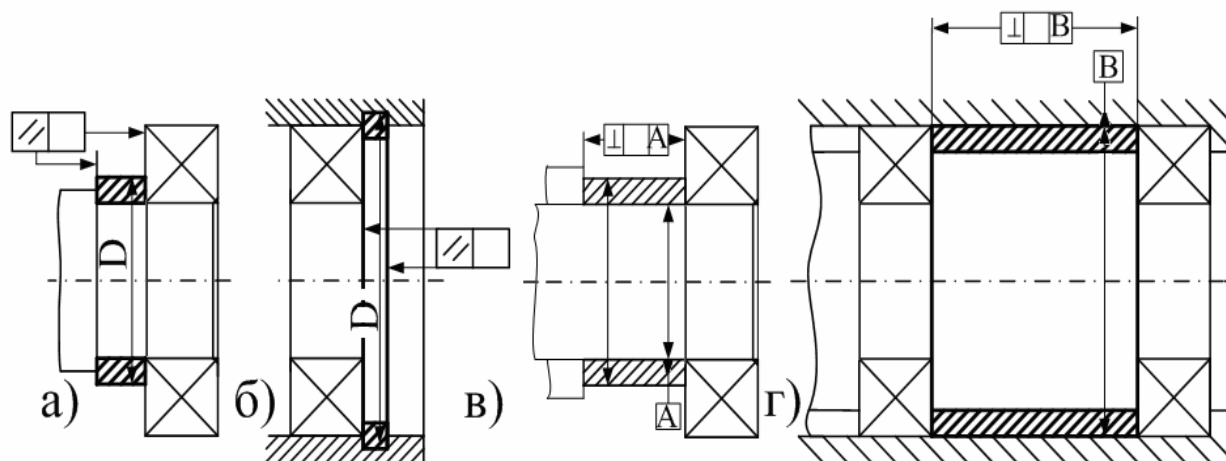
Допуски розташування втулок і кілець
